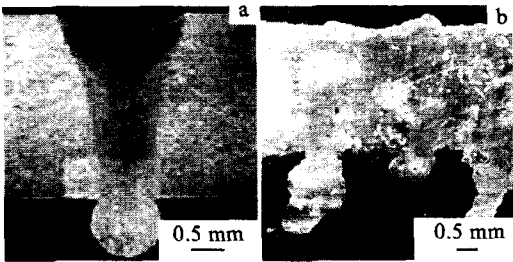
AZ31B 激光焊无背部气保护时焊缝横、纵截面形貌
